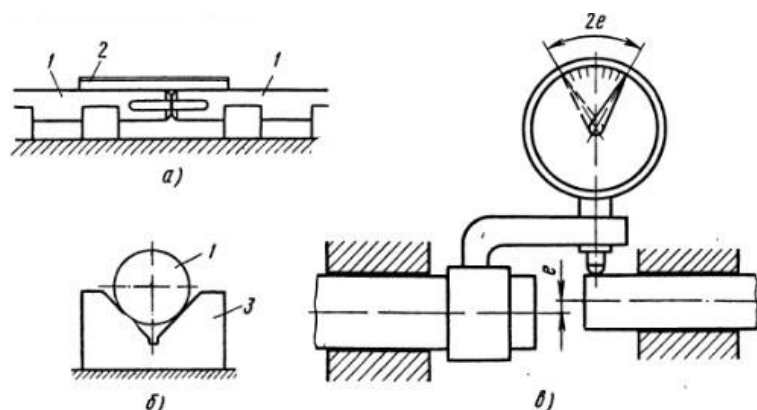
Проверка соосности валов: а — линейкой, б — призматической опорой, в — индикаторным приспособлением; 1 — вал, 2 — линейка, 3 — опора
